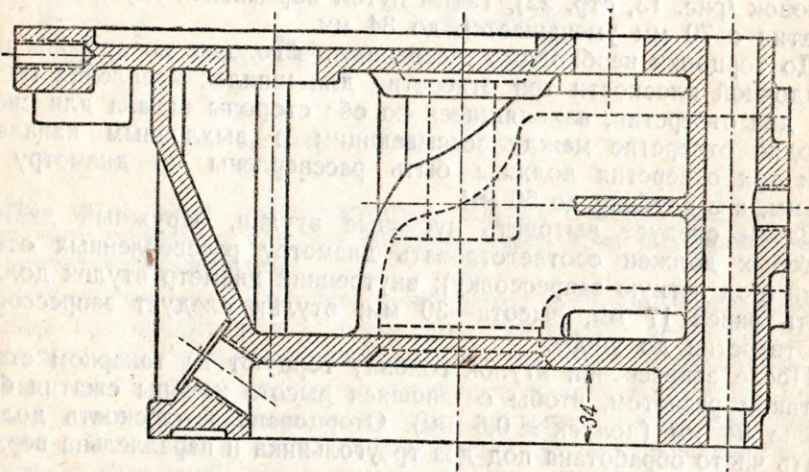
Головка лигроинового двигателя трактора «сталинец-60», переделанная для работы на древесном газе
